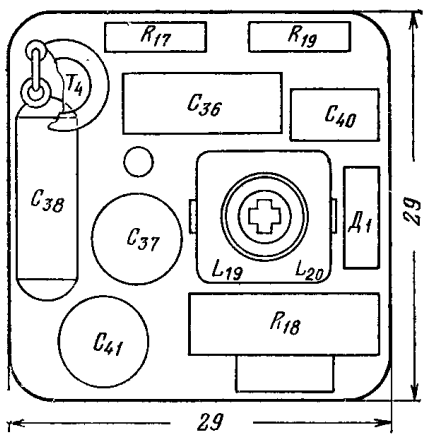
Схема расположения узлов и деталей на печатной плате блока ПЧД приемника «Спорт-2»
